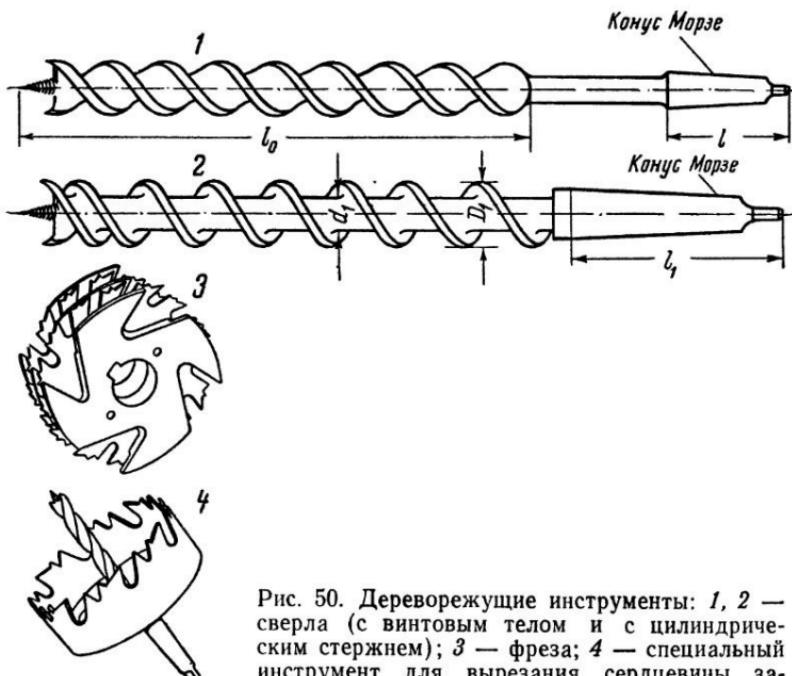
Дереворежущие инструменты: 1, 2 — сверла (с винтовым телом и с цилиндрическим стержнем); 3 — фреза; 4 — специальный инструмент для вырезания сердцевины заготовки.
